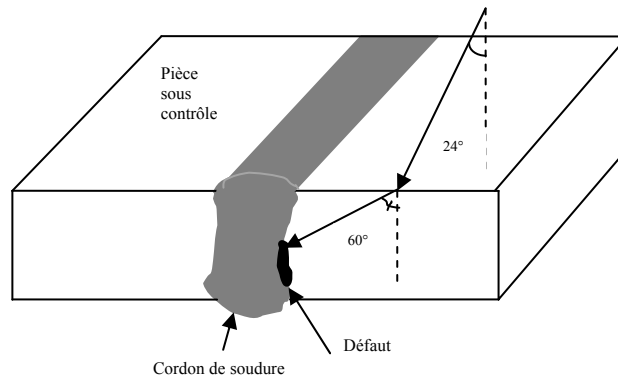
Bloc expérimental dans lequel un cordon de soudure inclut un défaut.
